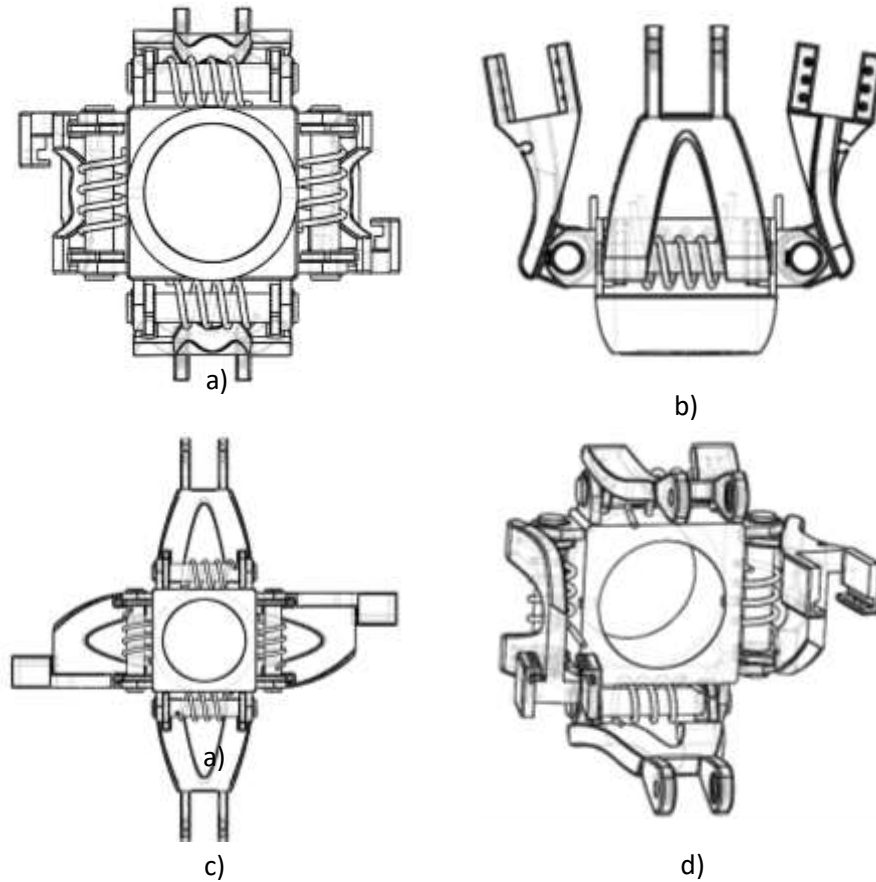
Diseño CAD de sistema adaptable al diámetro. a) Vista frontal b) Vista superior c) Vista posterior d) Vista isométrica
